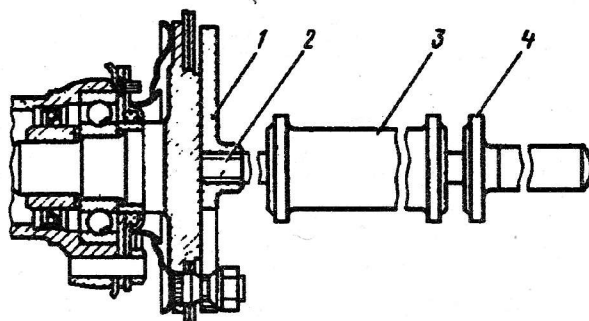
Выпрессовка полуоси съемником 7823-6091:
